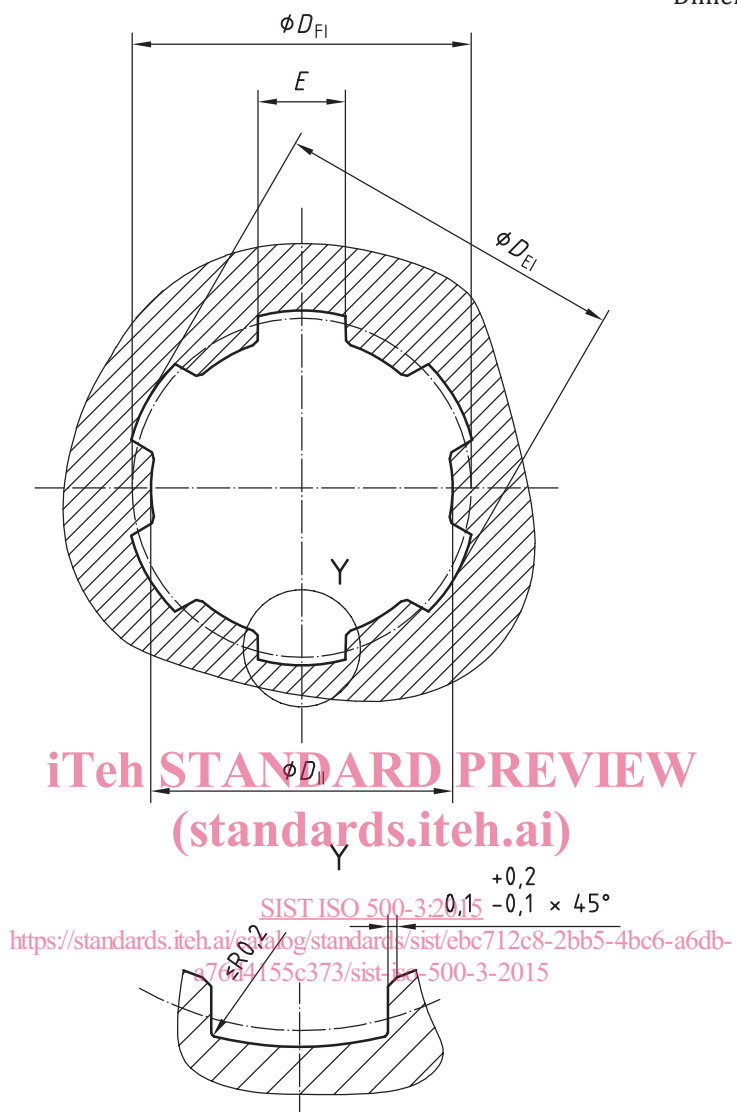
Dimensions des cannelures à flancs droits internes — Type 1
